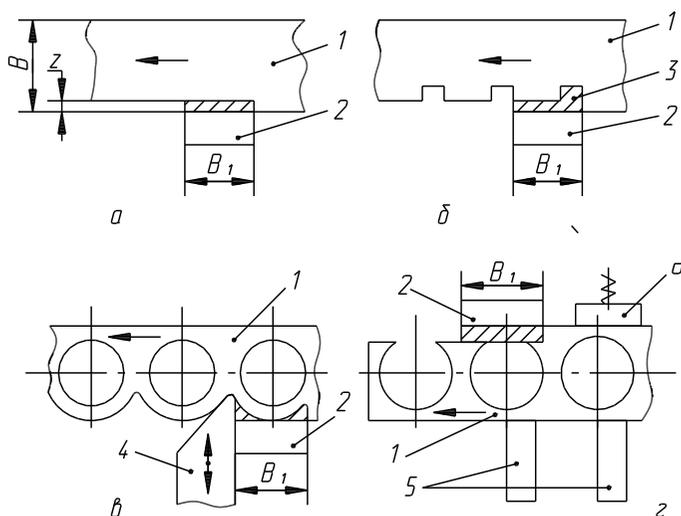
Конструктивные формы шаговых ложей: 1 — полоса, 2 — шаговый нож, 3 — выступ для предотвращения образования «усика», 4 — подвижной упор, 5 — временные упоры, 6 — боковой прижим
